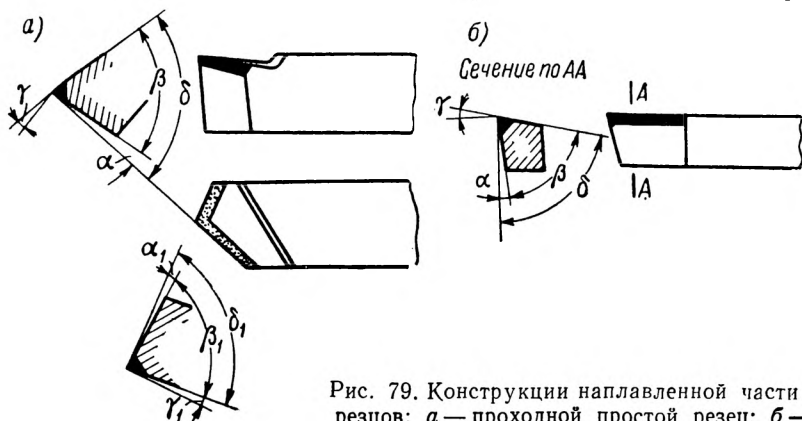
Конструкции наплавленной части резцов: а — проходной простой резец; б — подрезной правый резец.
